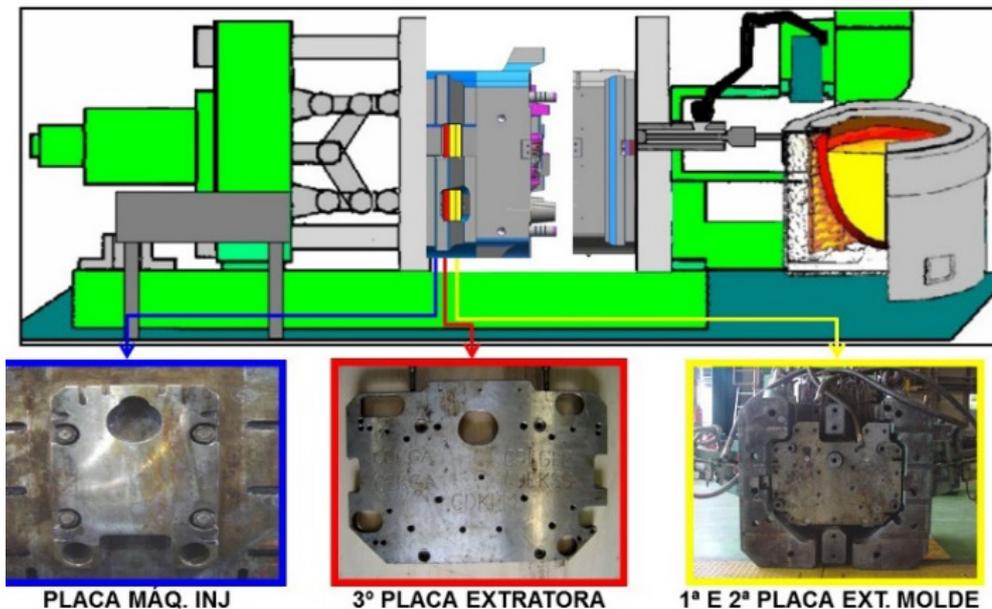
Detalhe das diferentes placas da máquina de injeção.
